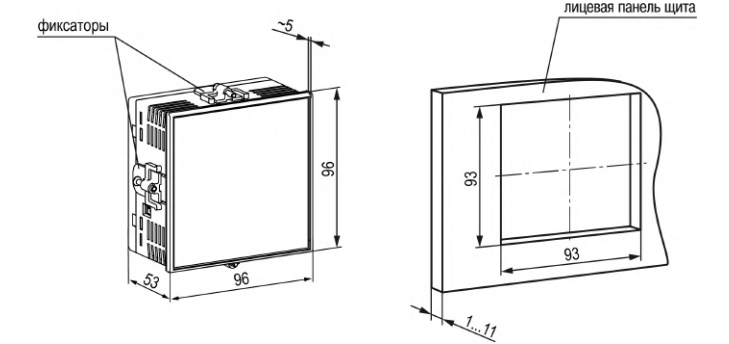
Габаритные размеры корпуса Щ1 и монтажного отверстия в щите
